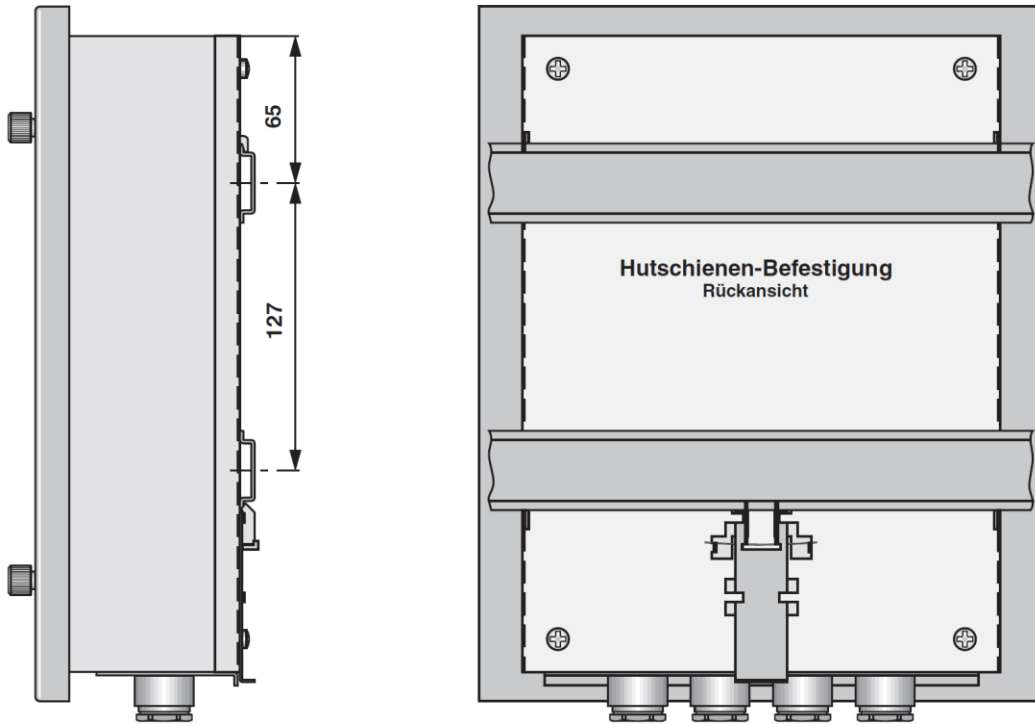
Mechanische Abmessungen, Hutschienenmontage
